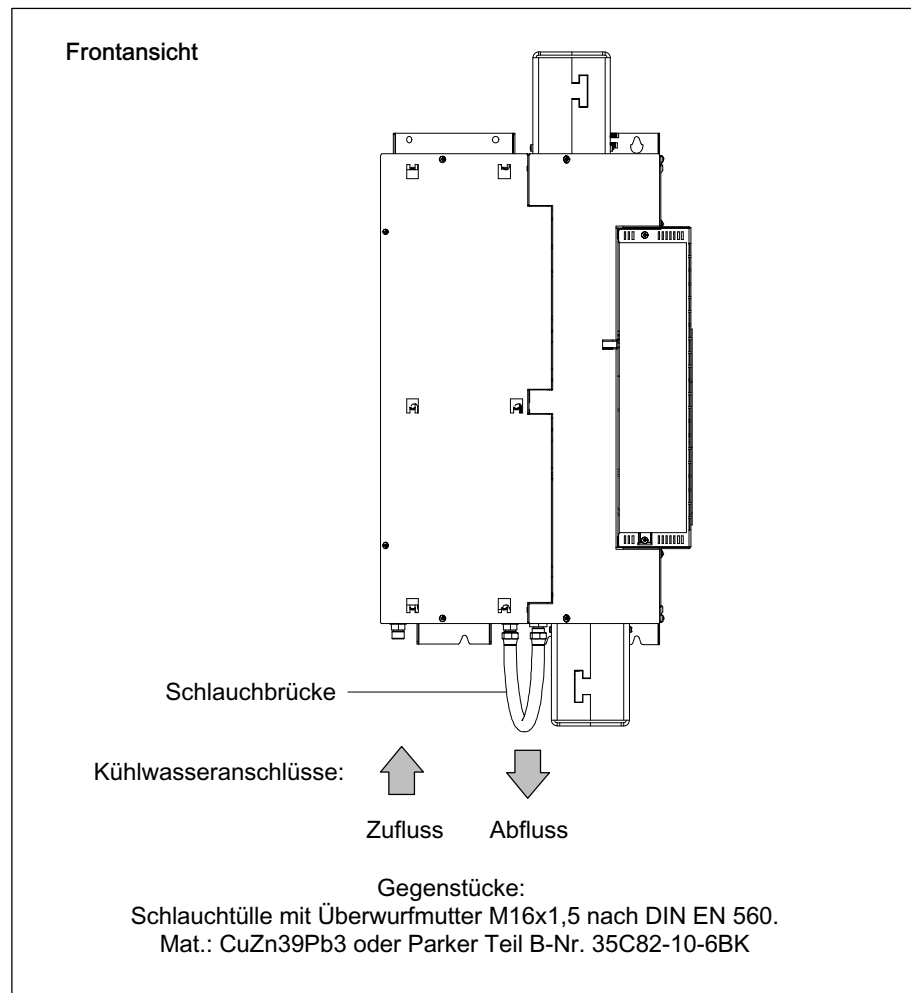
Position Kühlwasseranschluss: PSI 65xx.xxx W1
